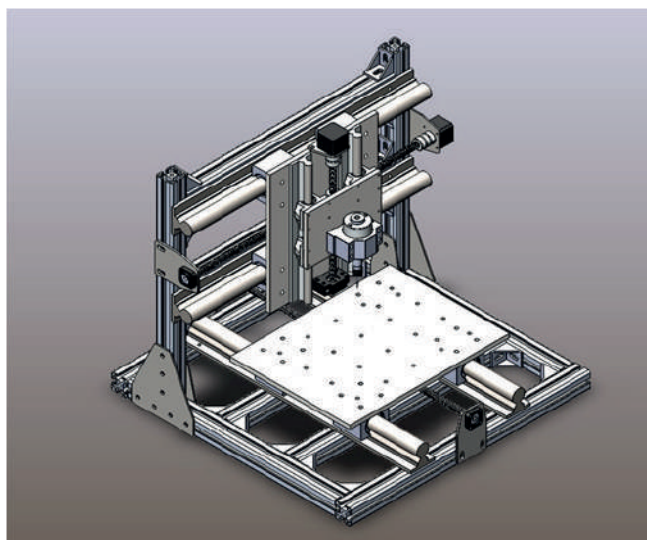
Модель фрезерного трехкоординатного портального станка с ЧПУ
